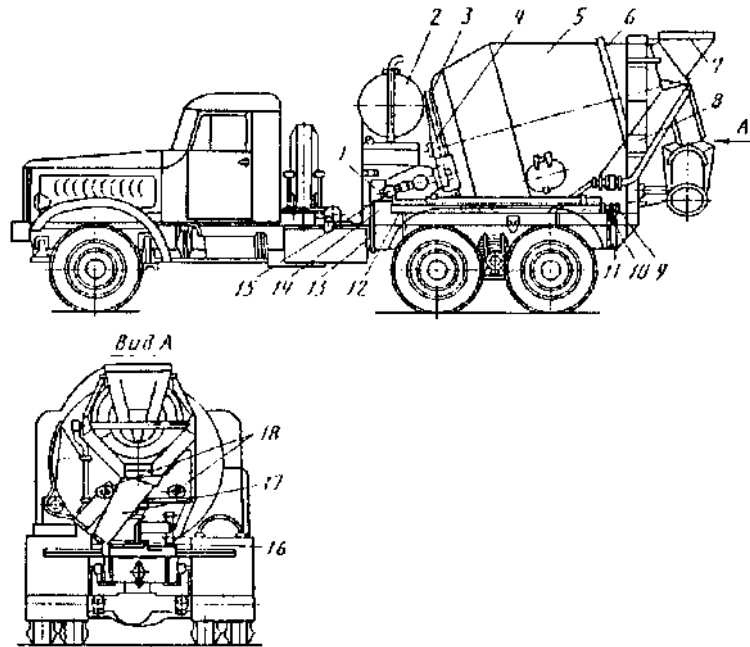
Автобетоносмеситель: 1 - рычаг управления декомпрессором; 2 - бак для воды; 3 - ведомая звездочка; 4 - главный подшипник барабана; 5 - смесительный барабан; 6 - бандаж; 7 - загрузочное устройство; 8 - лестница; 9 - рычаг управления муфтой сцепления; 10 - рычаг управления подачей топлива; 11 - рычаг управления механизмом реверсирования редуктора; 12 - рама; 13 - шасси; 14 - контрольно-измерительная аппаратура; 15 - редуктор привода барабана; 16 - устройство для поворота лотка; 17 - лоток; 18 - опорные ролики
